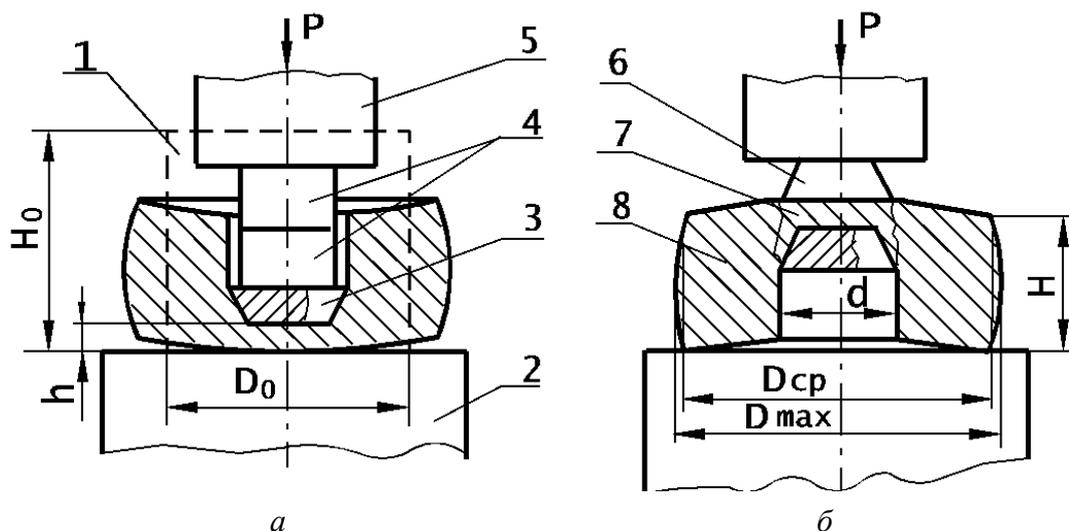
Схема прошивки сплошным прошивнем: а – прошивка; б – просечка; 1 – заготовка; 2, 5 – бойки; 3 – прошивень; 4 – надставка; 6 – прошивень просечной; 7 – выдра; 8 – прошитая поковка
